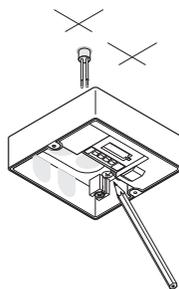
Разметка отверстий для крепления на поверхность
